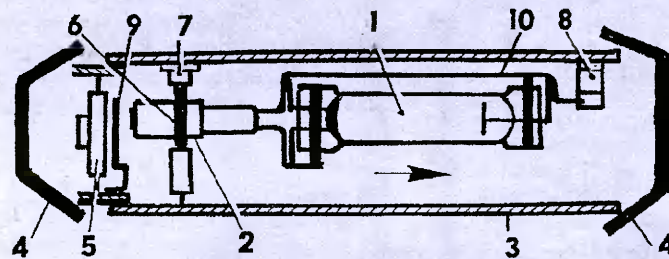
Конструкция озонатора: 1 — излучатель; 2 — электропатрон; 3 — труба; 4 — светозащитные конусы; 5 — вентилятор; 6 — хомут; 7 — стойка задняя, 2 шт.; 8 — стойка передняя, 1 шт.; 9 — экран вентилятора; 10 — стержень излучателя.
